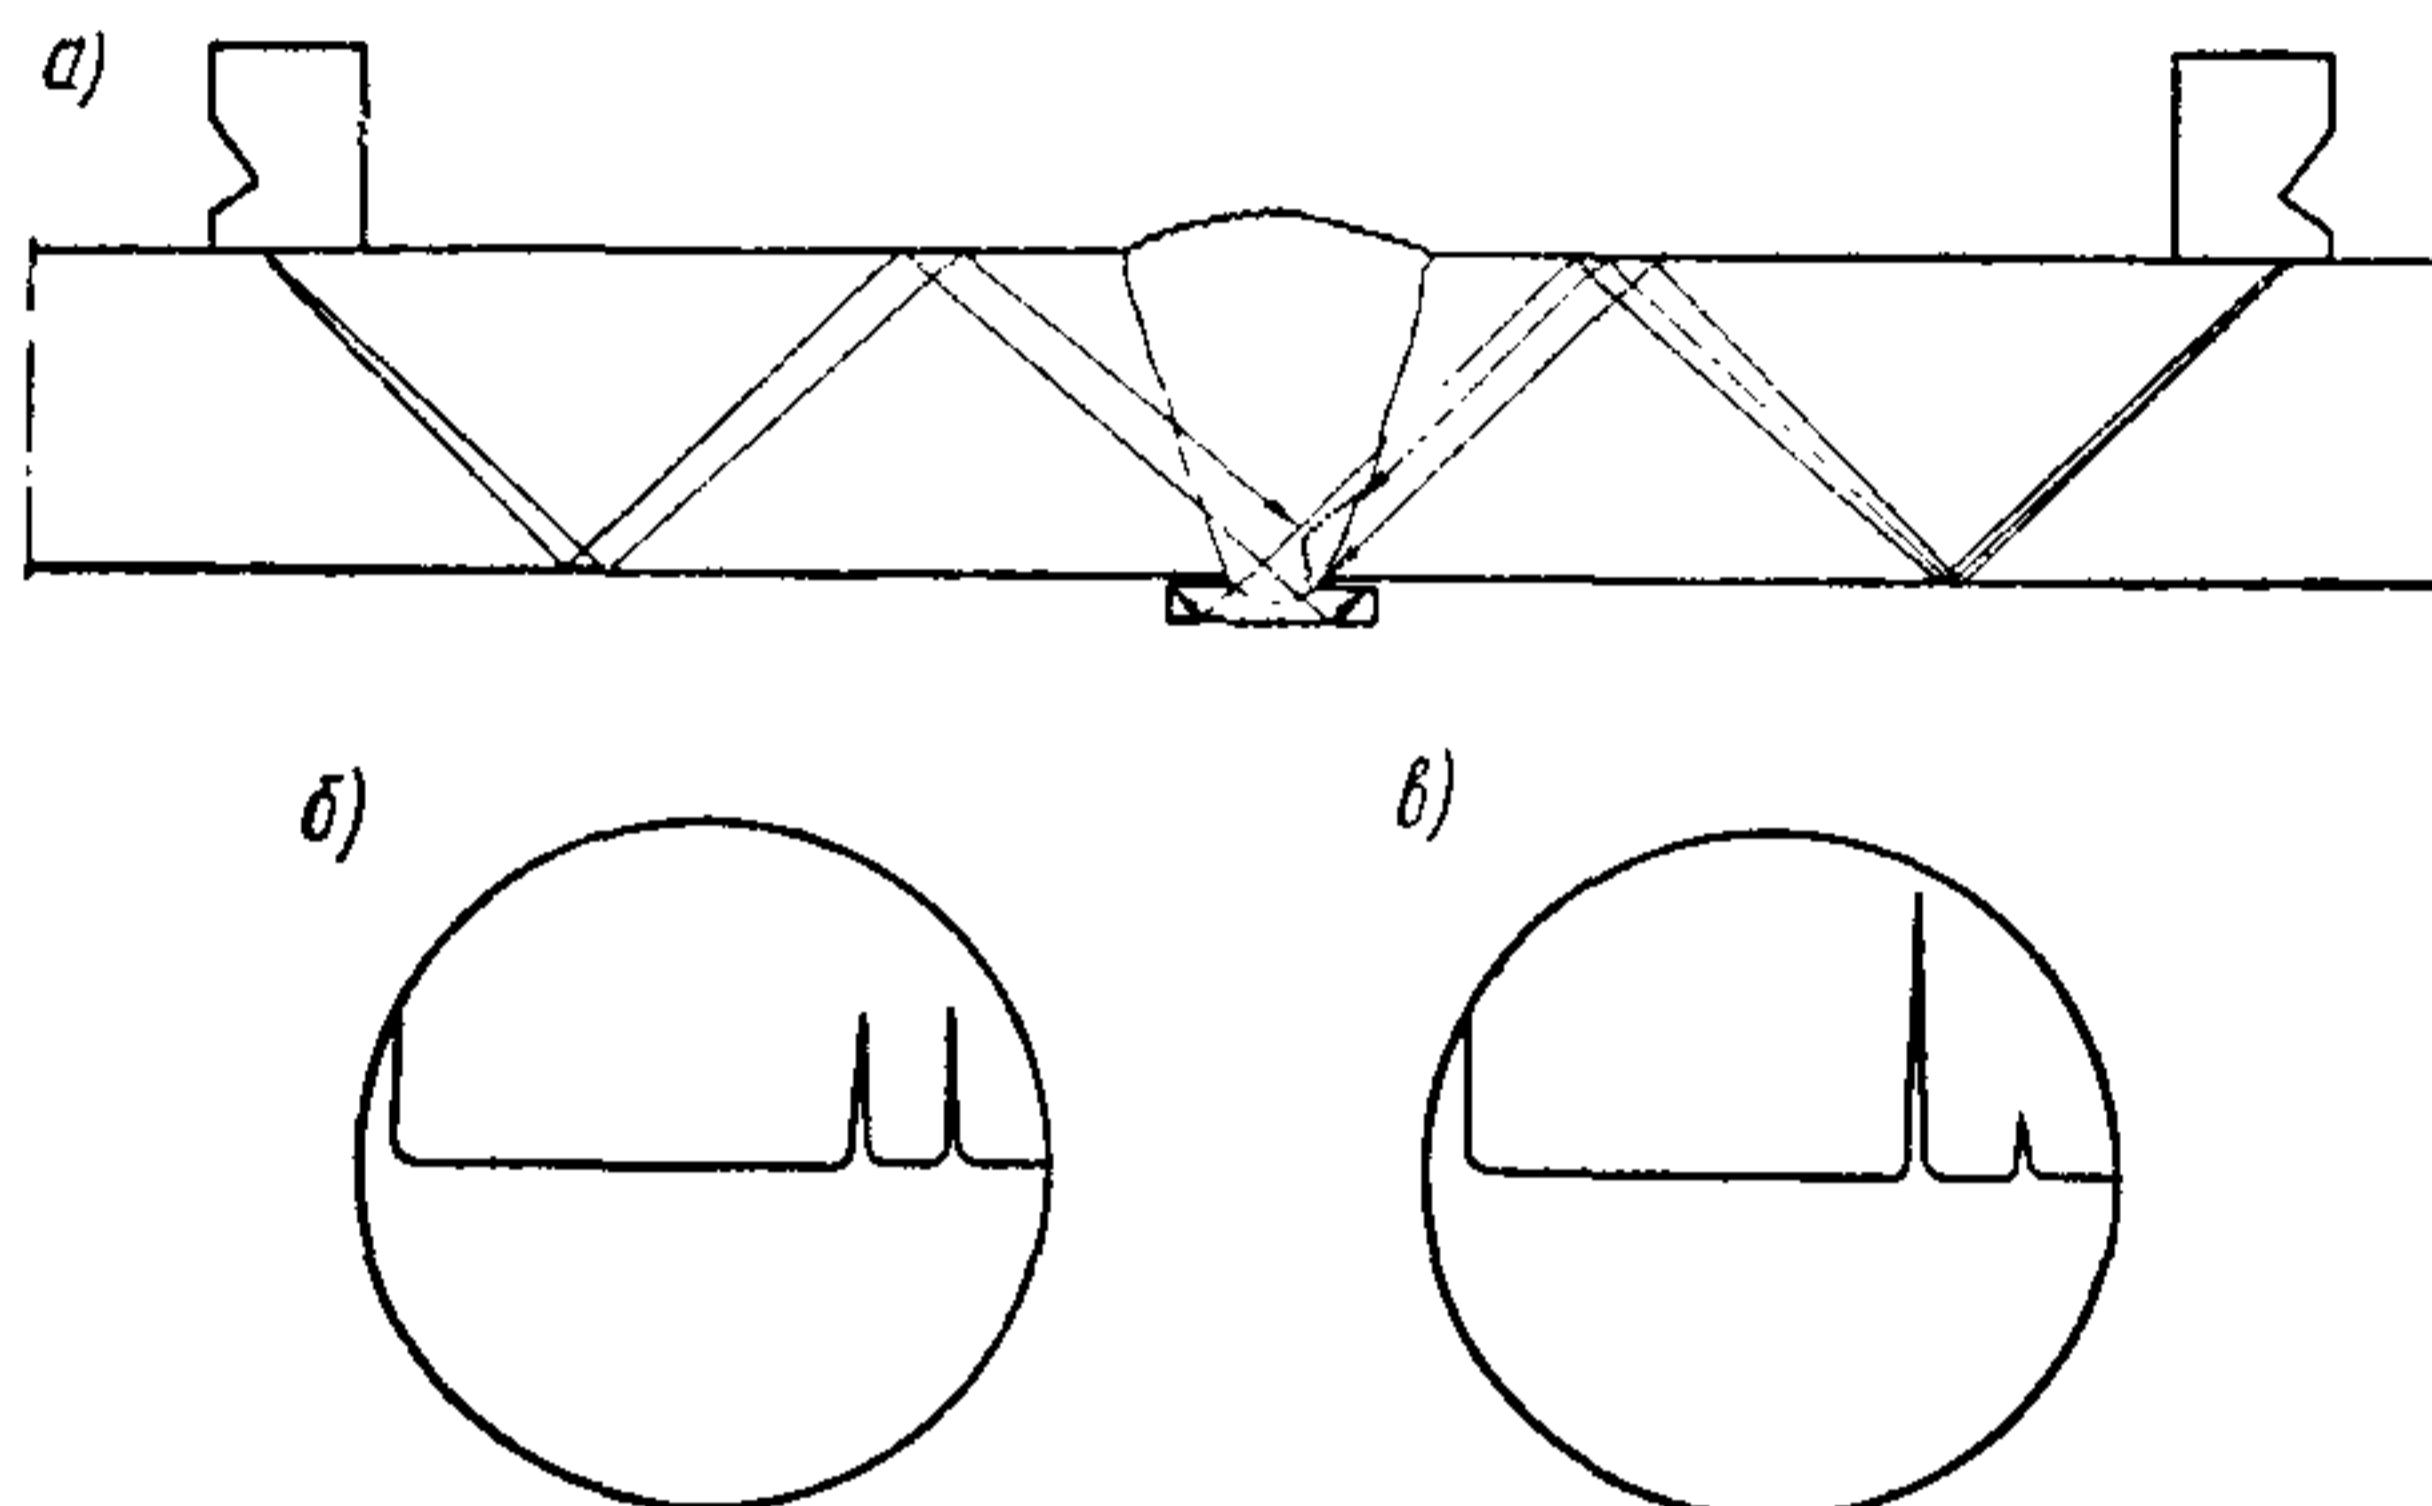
Контроль сварного стыка с частичным непроваром корня шва глубиной менее 3 мм
